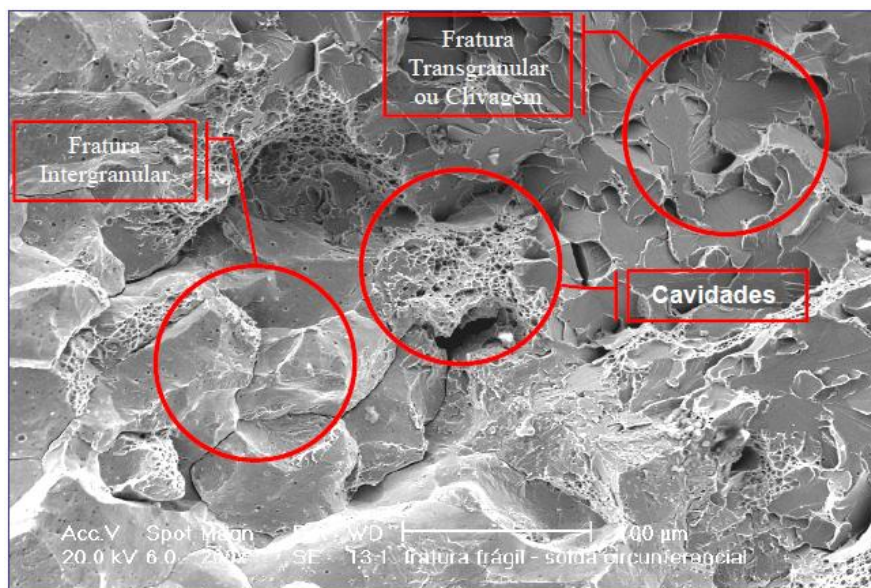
Modo de fratura combinada: com regiões de clivagem, intergranular e alveolar – Effting, 2004.
